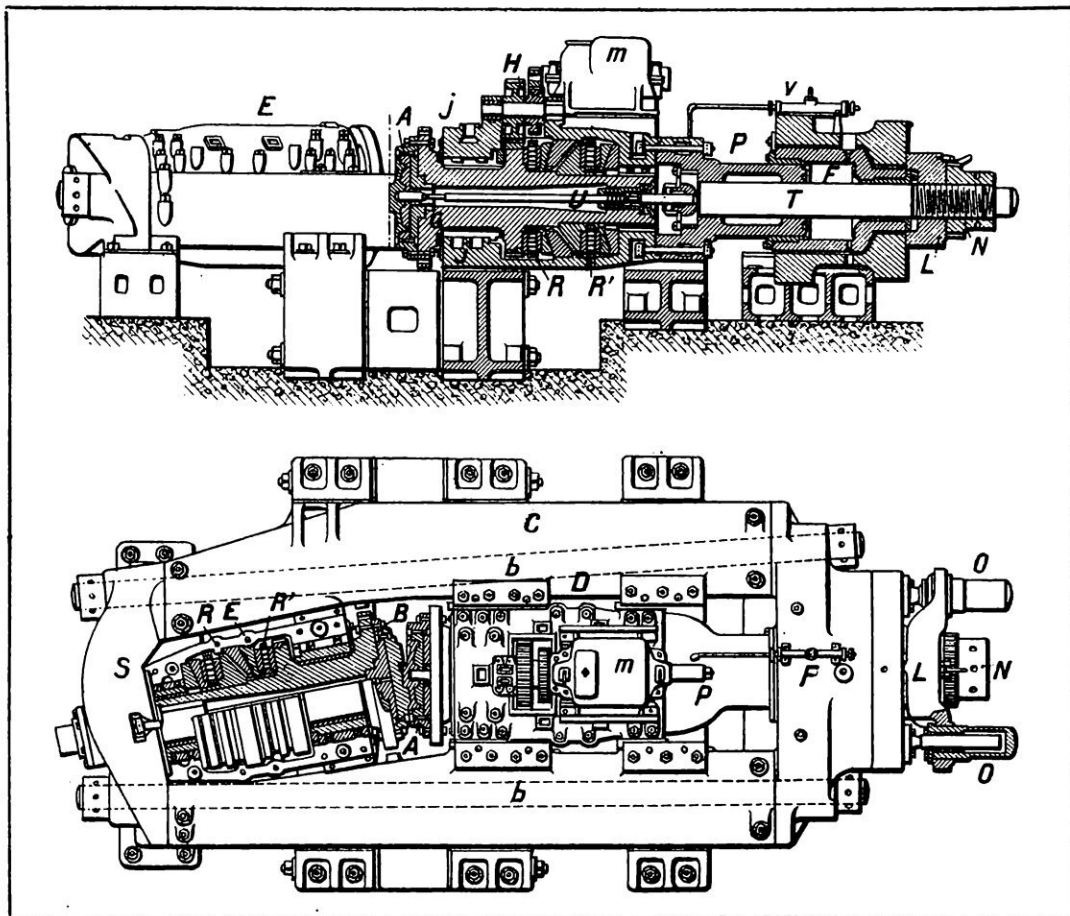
COUPE VERTICALE ET PLAN DU LAMINOIR A ROUES SLICK
